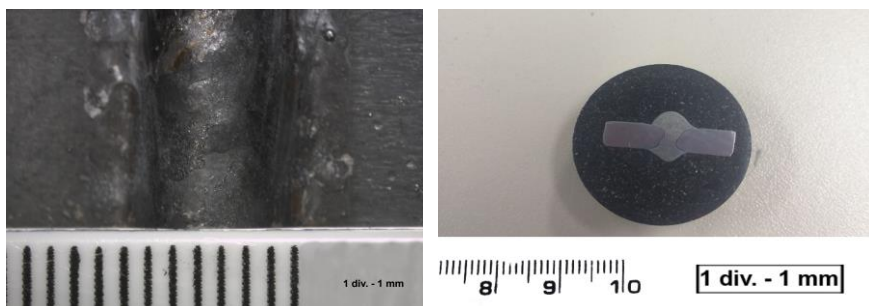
Detalhe superfície e perfil do cordão de solda do corpo de prova 3.
